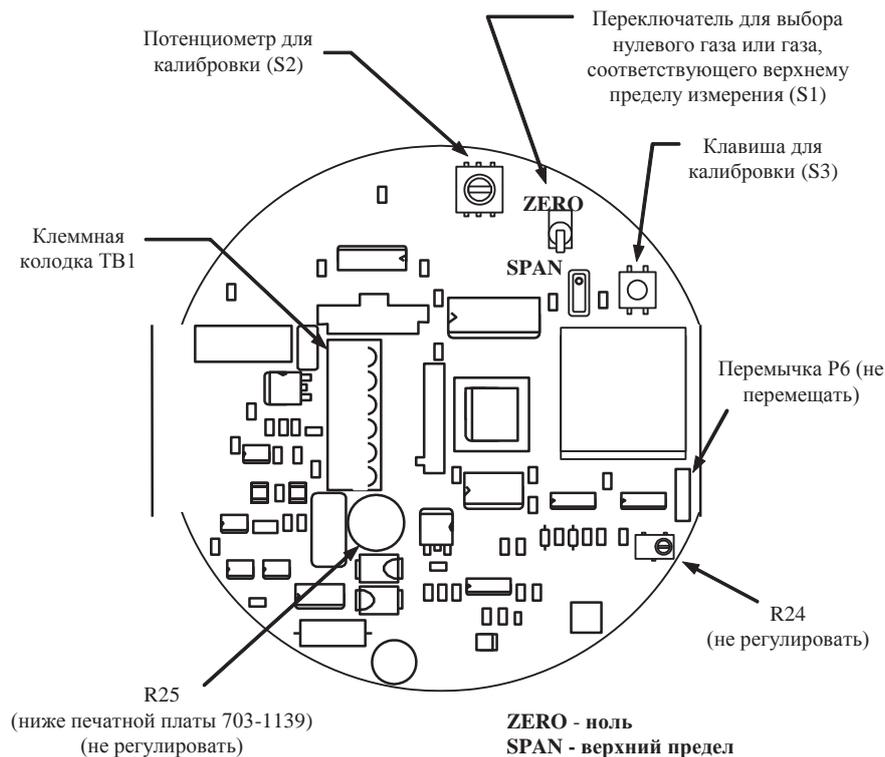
Расположение калибровочных переключателей на печатной плате 703-1139
